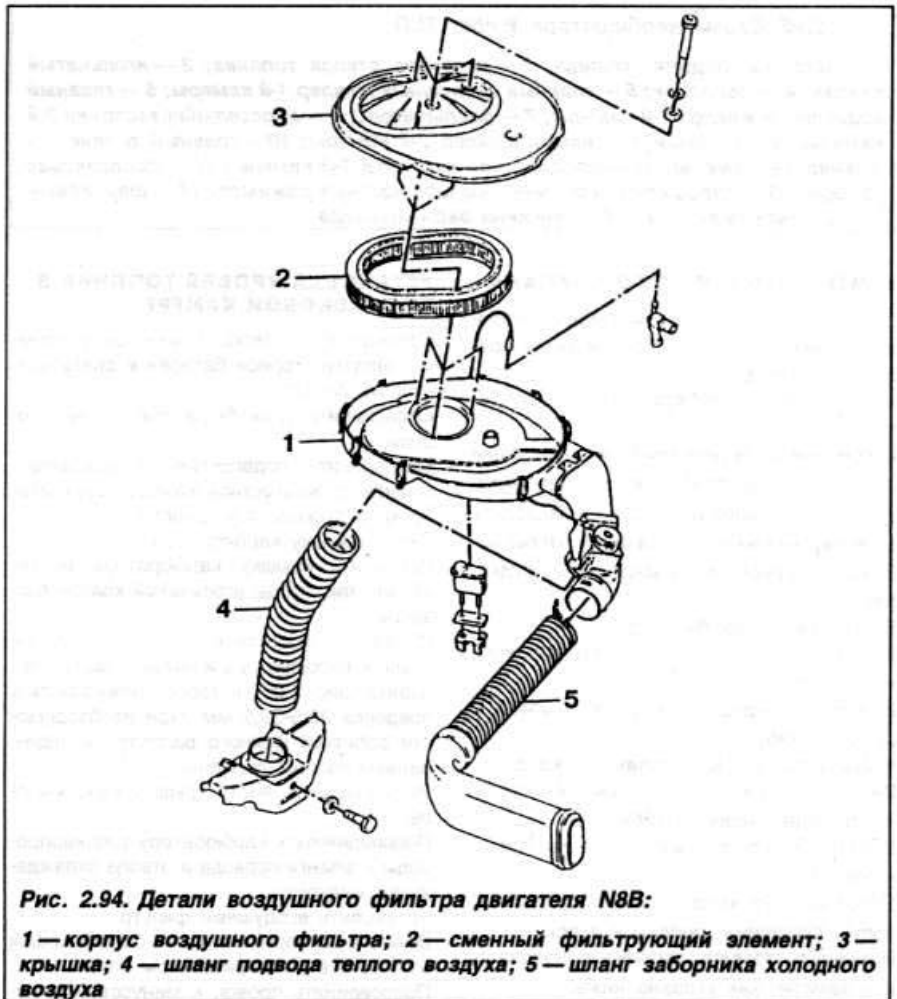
Детали воздушного фильтра двигателя N8B:
